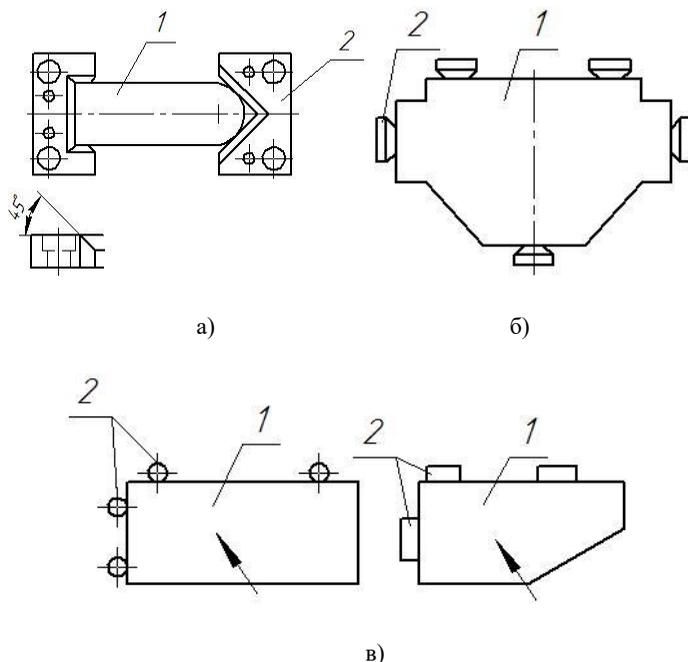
Фиксаторы: а – для вырубленных заготовок малых и средних размеров; б – для вырубленных заготовок крупных размеров; в – для заготовок, отрезанных на ножницах; 1 – заготовка; 2 – фиксаторы
